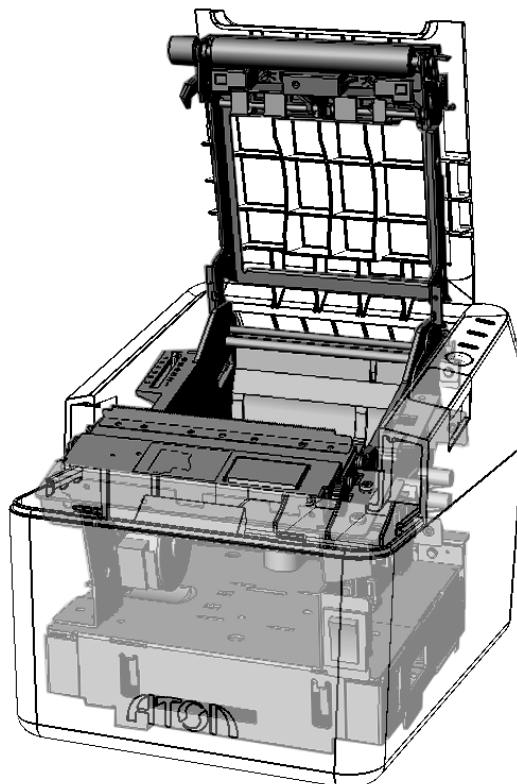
Термопечатающий механизм с автоотрезом PRT-TP803 в корпусе ККТ
